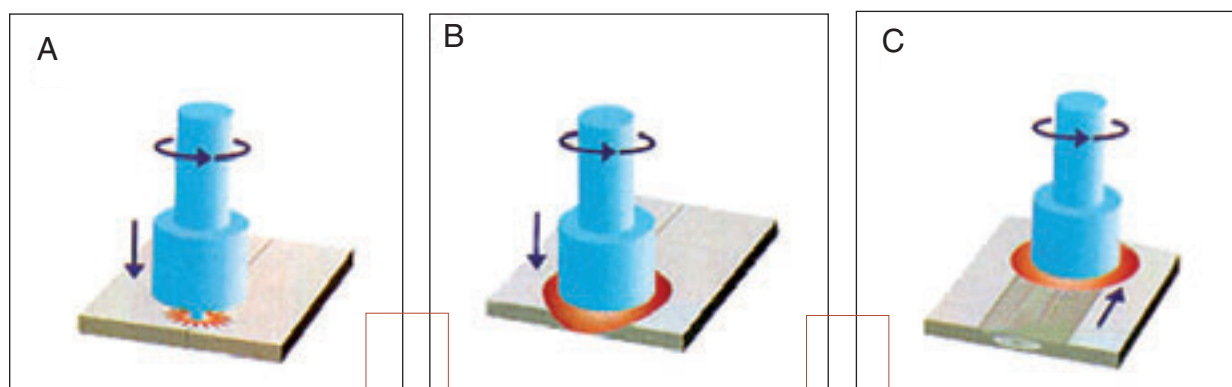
Fasi del processo Friction Stir Welding (FSW).
